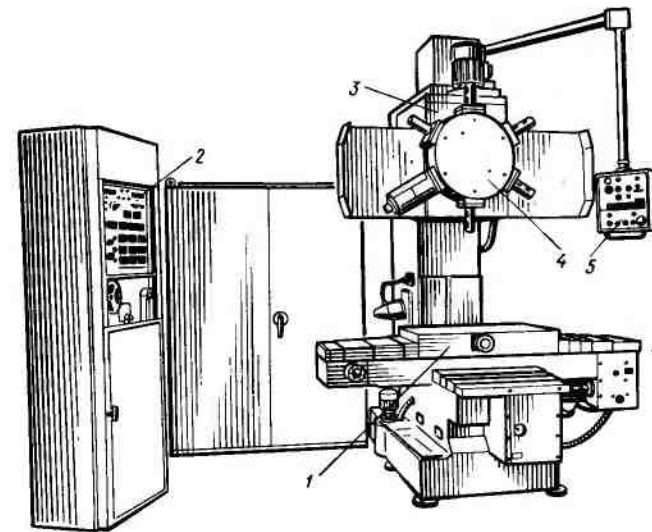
Сверлильный станок мод. 2Р135Ф2
